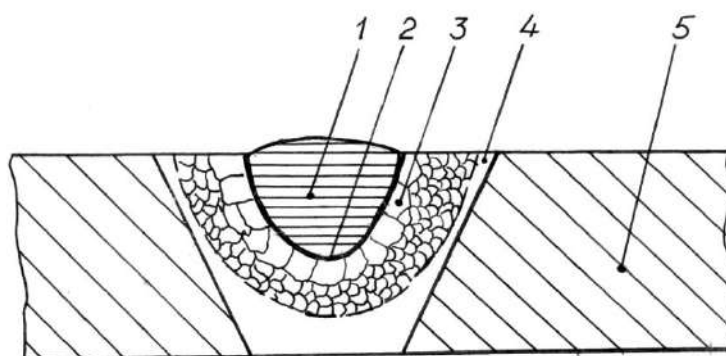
Аргонодуговая подварка непротяженного несплавления в шве сплава 1565чМ, полученного сваркой трением с перемешиванием
